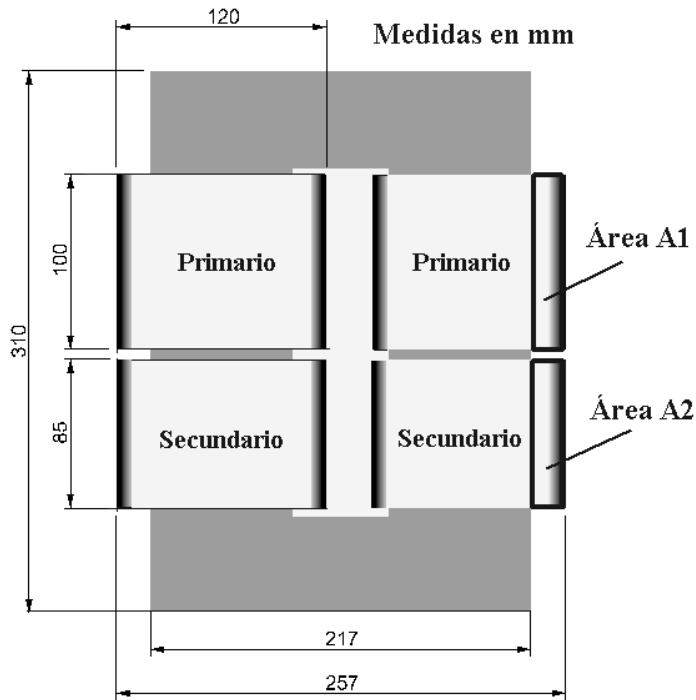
Corte de una bobina de aluminio encapsulada en resina
